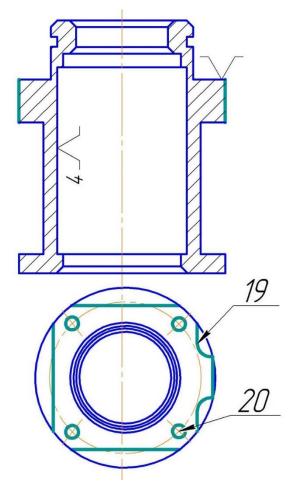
Эскиз для фрезерной операции с ЧПУ
